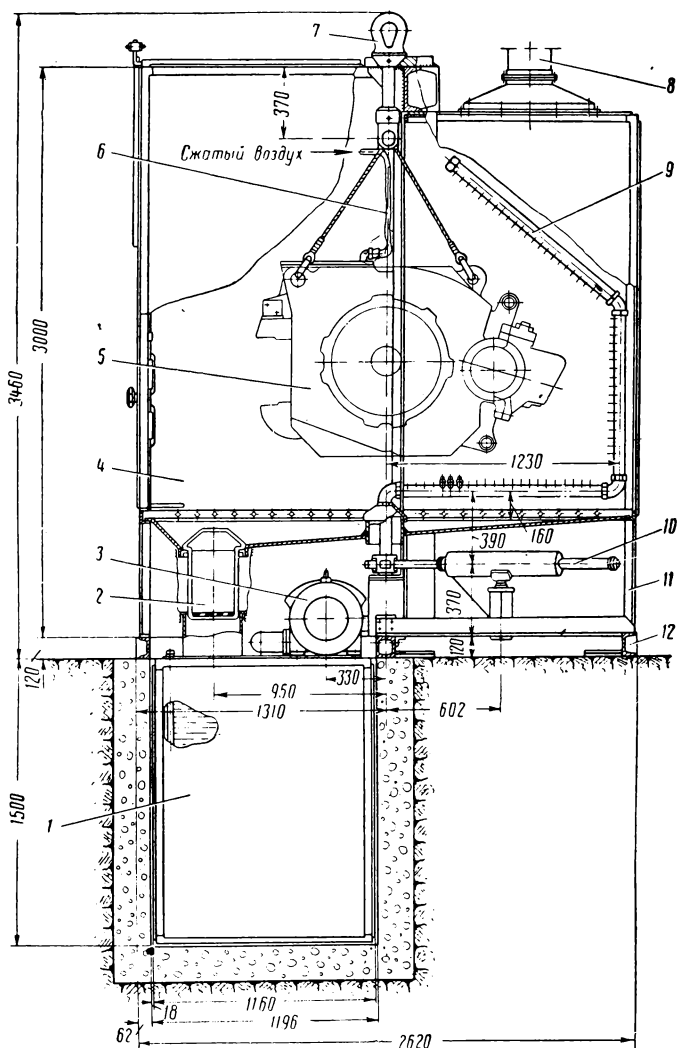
Установка для предварительной наружной очистки машин до разборки:
